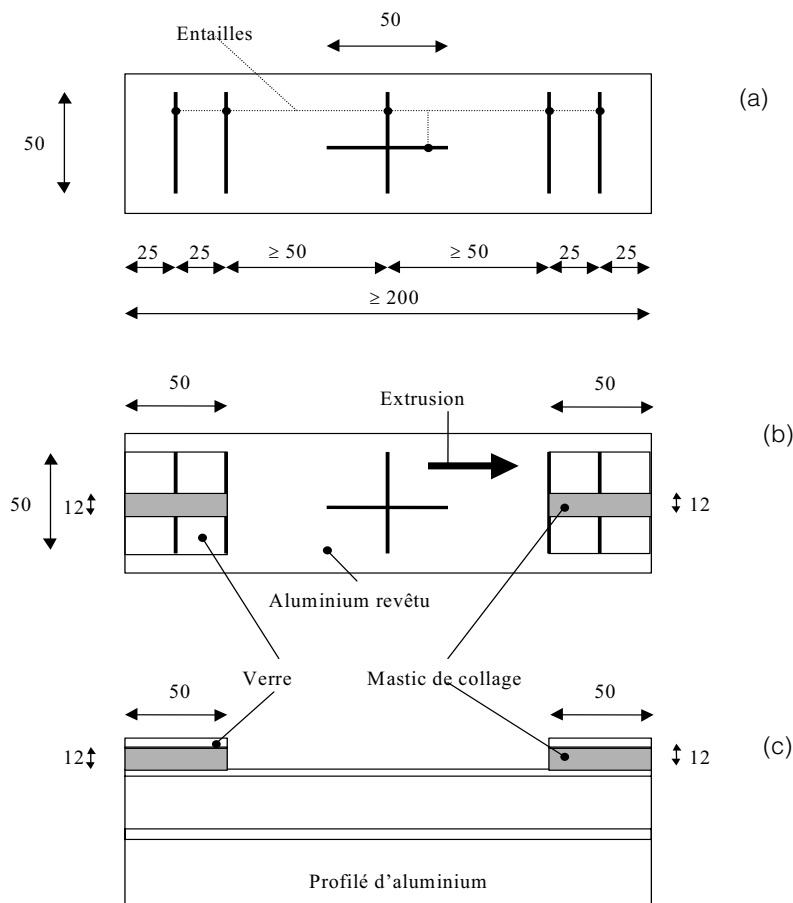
(Ajout 1) – Éprouvette pour essais de corrosion filiforme
